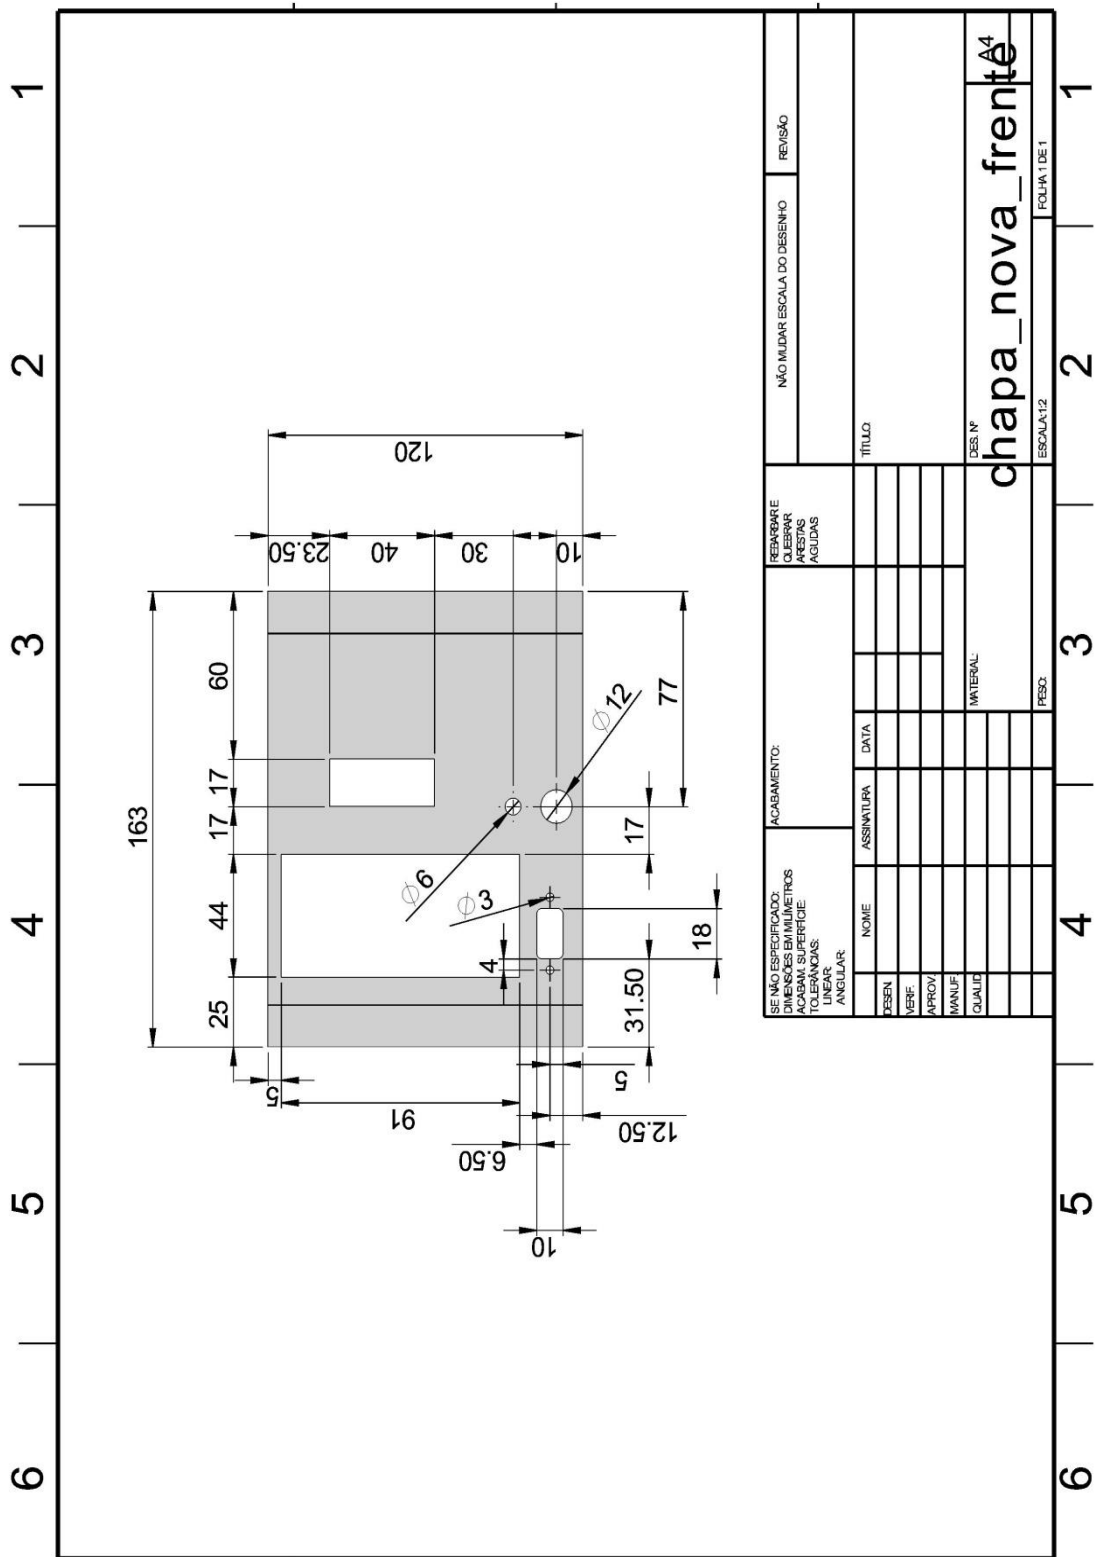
Desenho técnico 2D da chapa frontal para a fixação do controlador, conector DB-9, fusível, chave de alavanca, e disjuntor.
